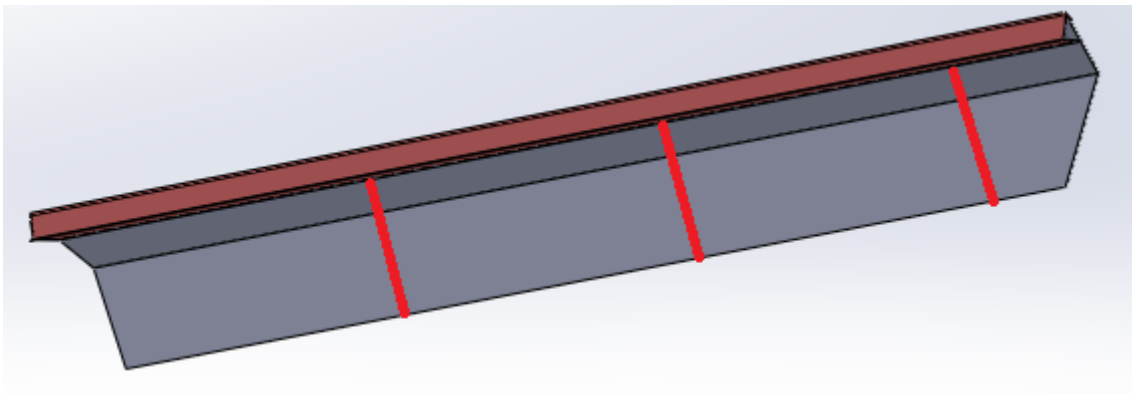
Vista trasera matriz de soldadura de frente.
